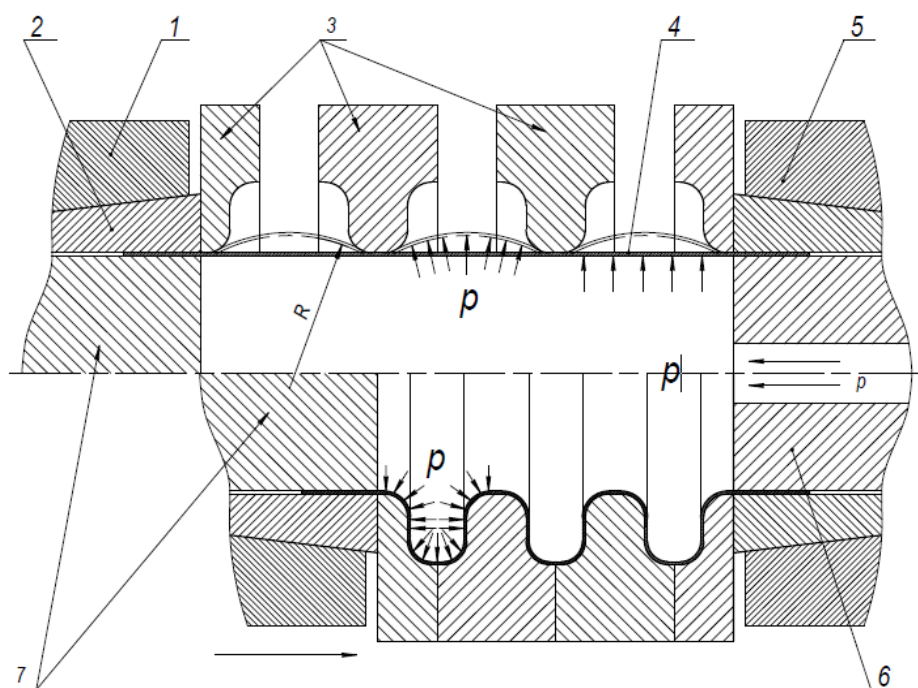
Спосіб формовки гідростатичним тиском рідини з середини заготовки
